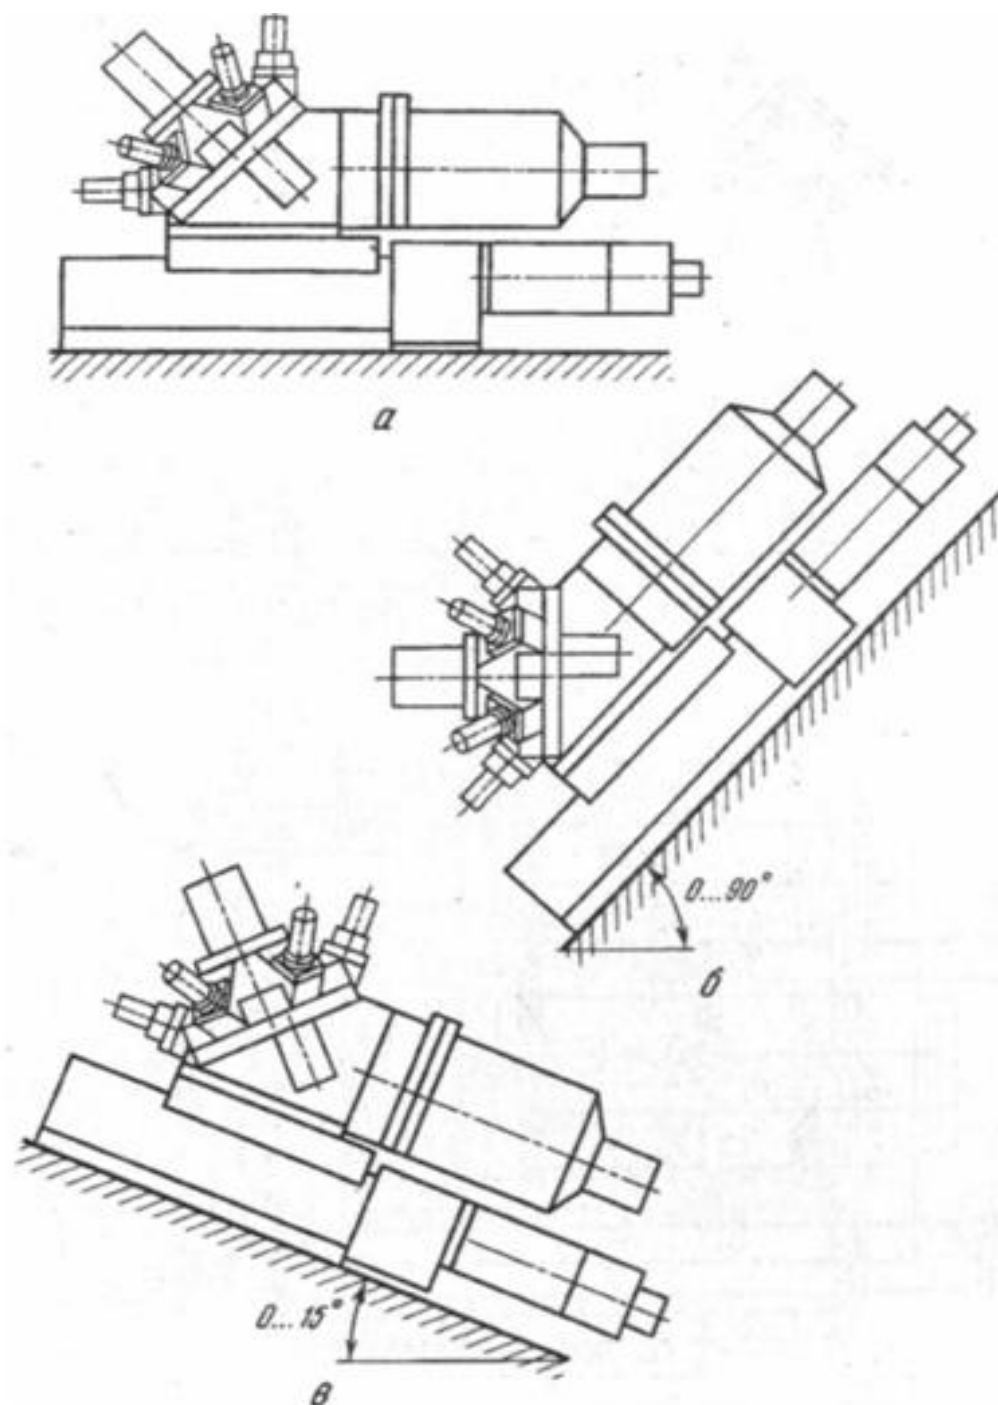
Варианты установки револьверных бабок: а – горизонтальная установка, б – наклонная установка с направлением рабочей подачи сверху вниз, в - наклонная установка с направлением рабочей подачи снизу вверх.
